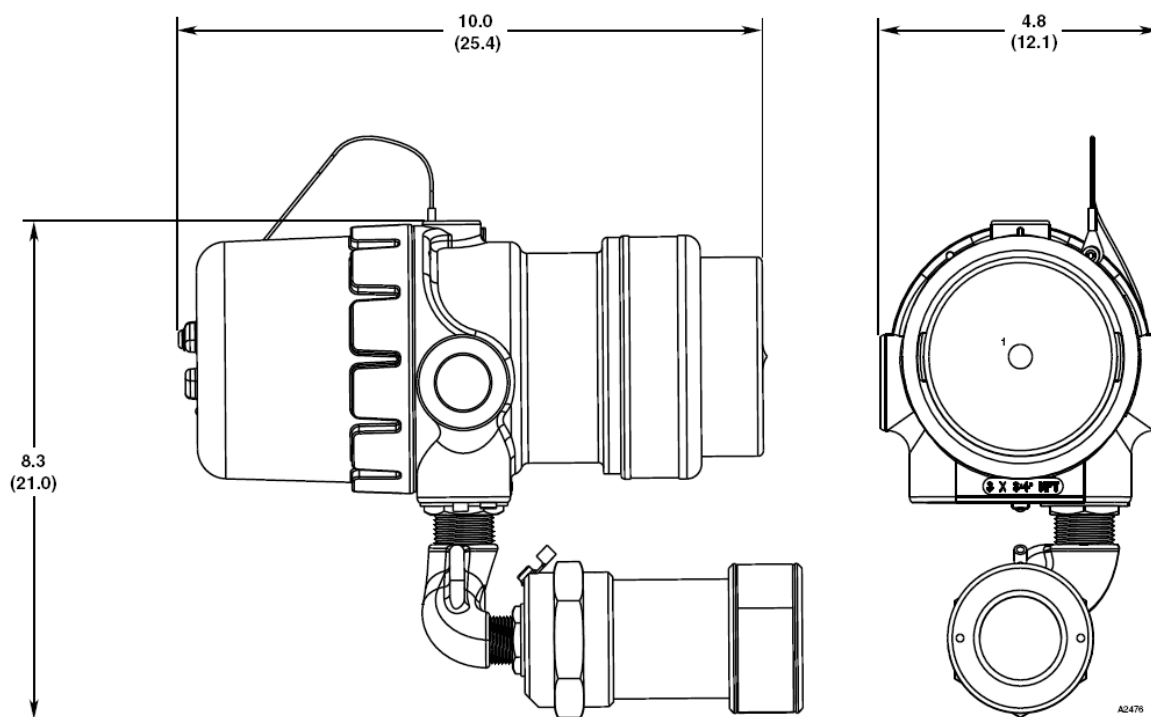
Габаритные размеры извещателя с видеокамерой в дюймах (см)
